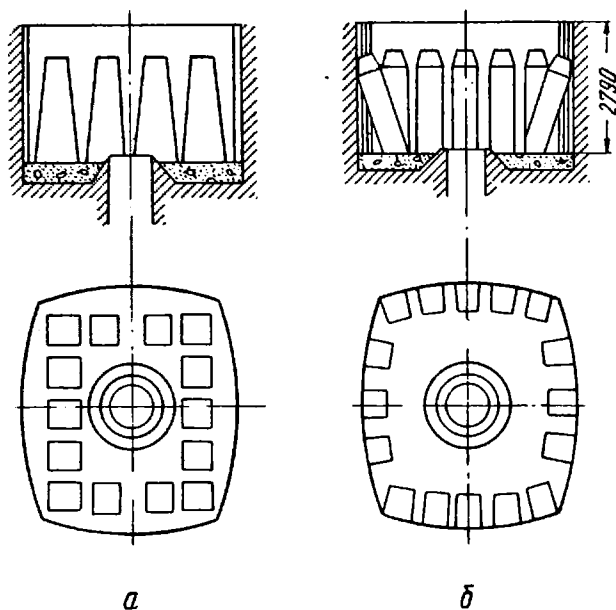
Схема размещения слитков в камерах рекуперативных нагревательных колодцев с отоплением из центра подины
